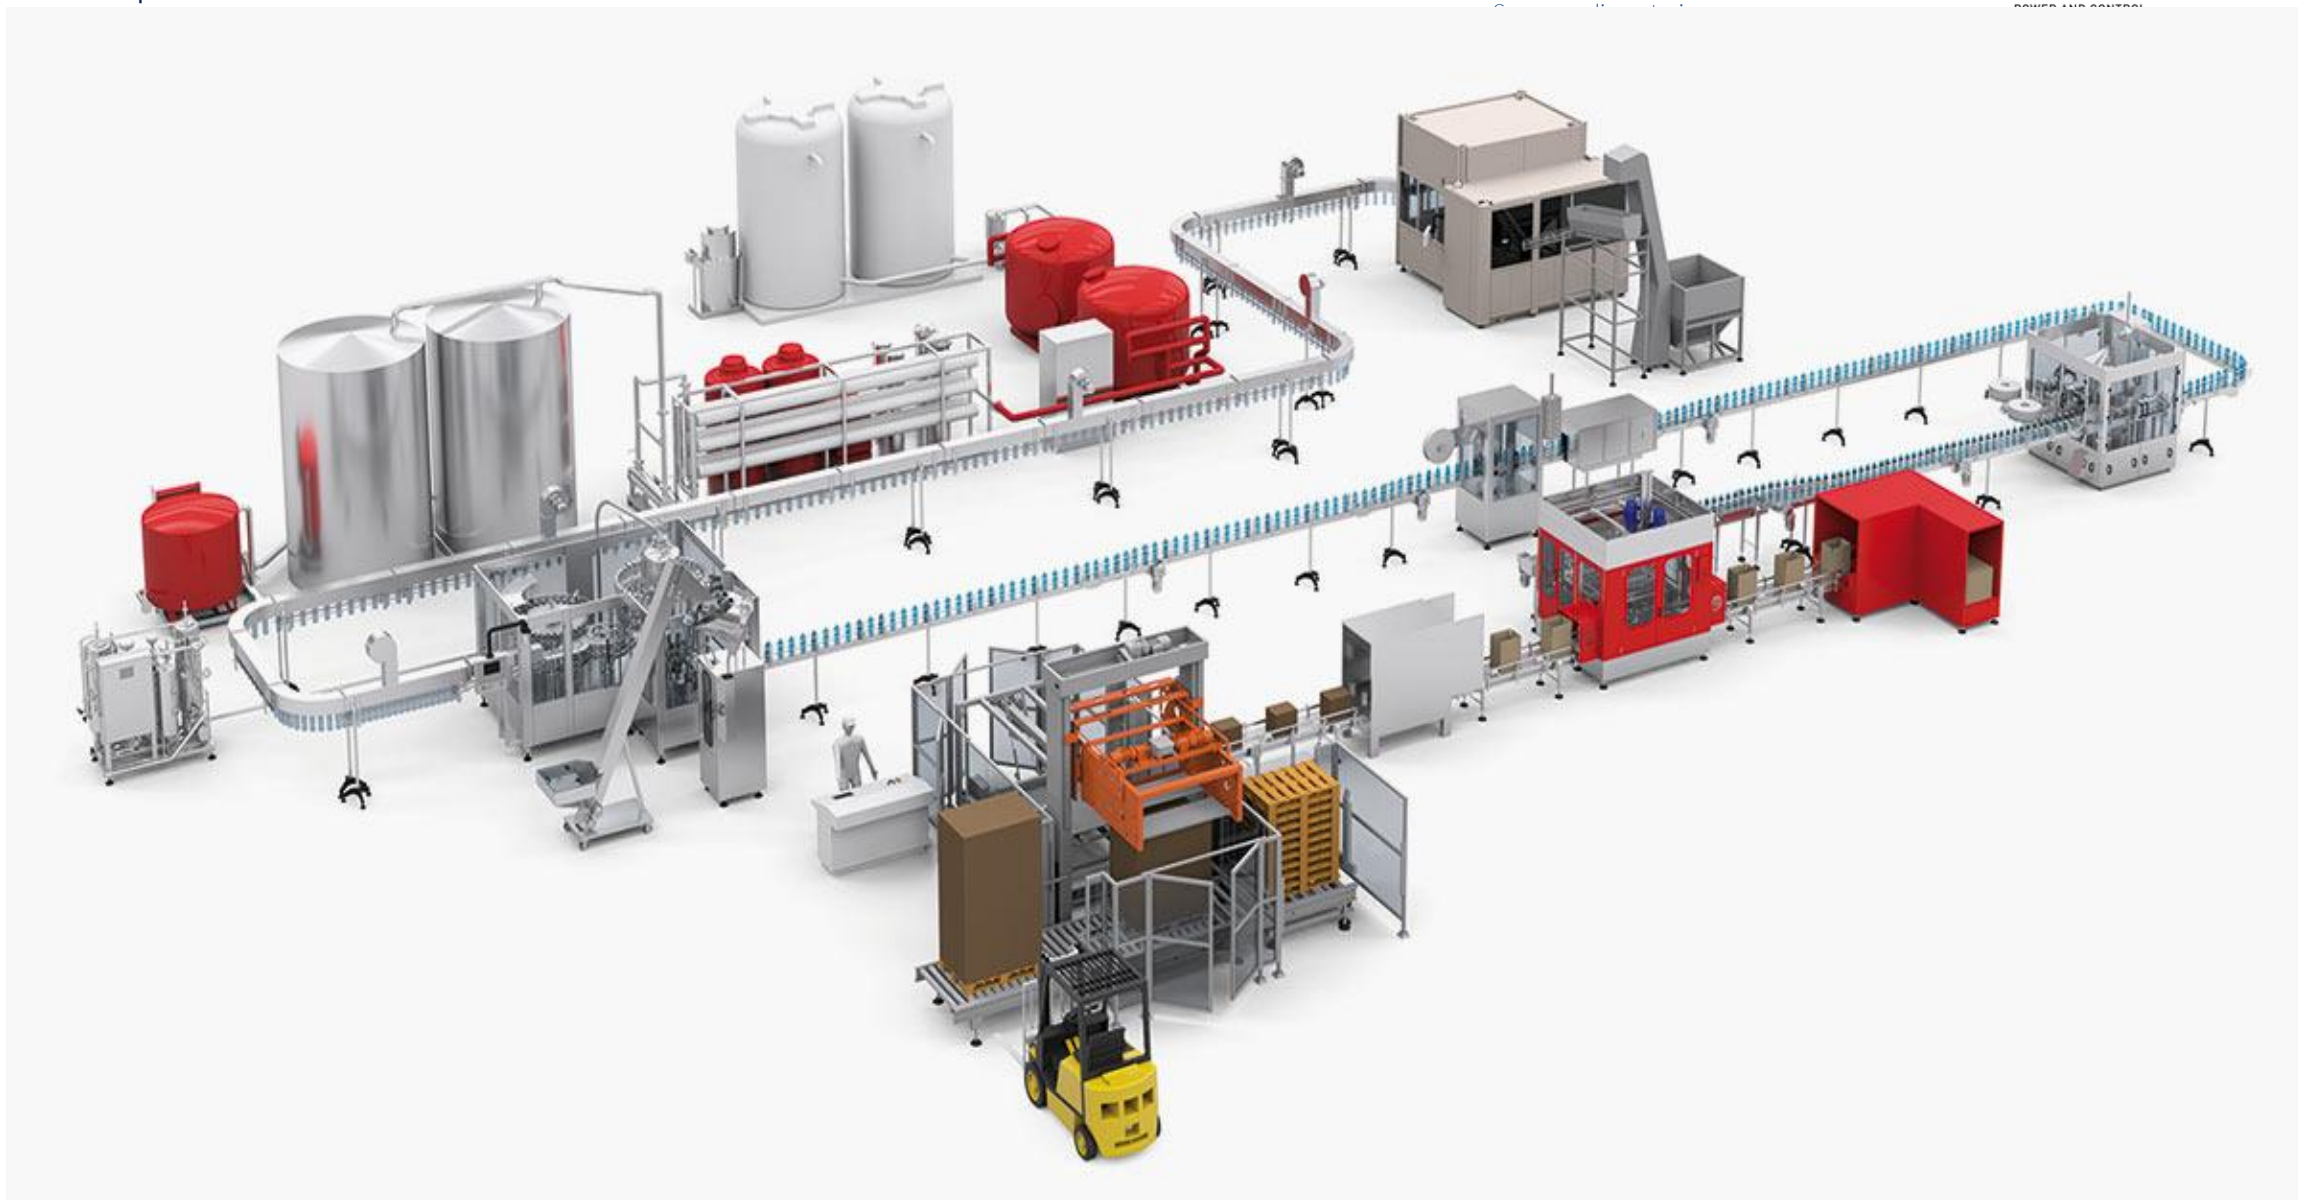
Inquadramento dell'impianto a notte nell'azienda (nell'Appendice F è disponibile la planimetria ad alta definizione)
